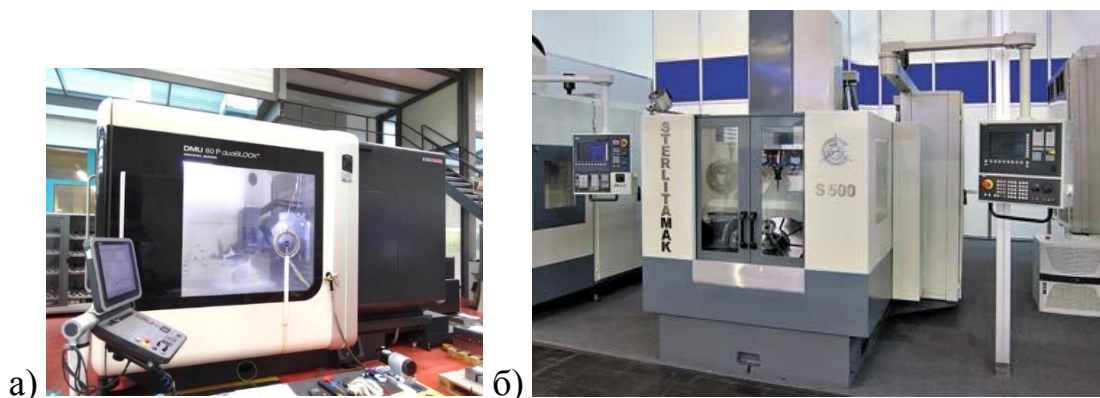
Установки, используемые для фрезерования стыкуемых кромок под сварку:
